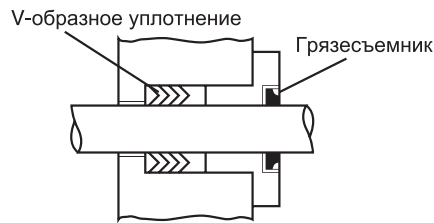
Уплотнения сальника штока гидроцилиндра
